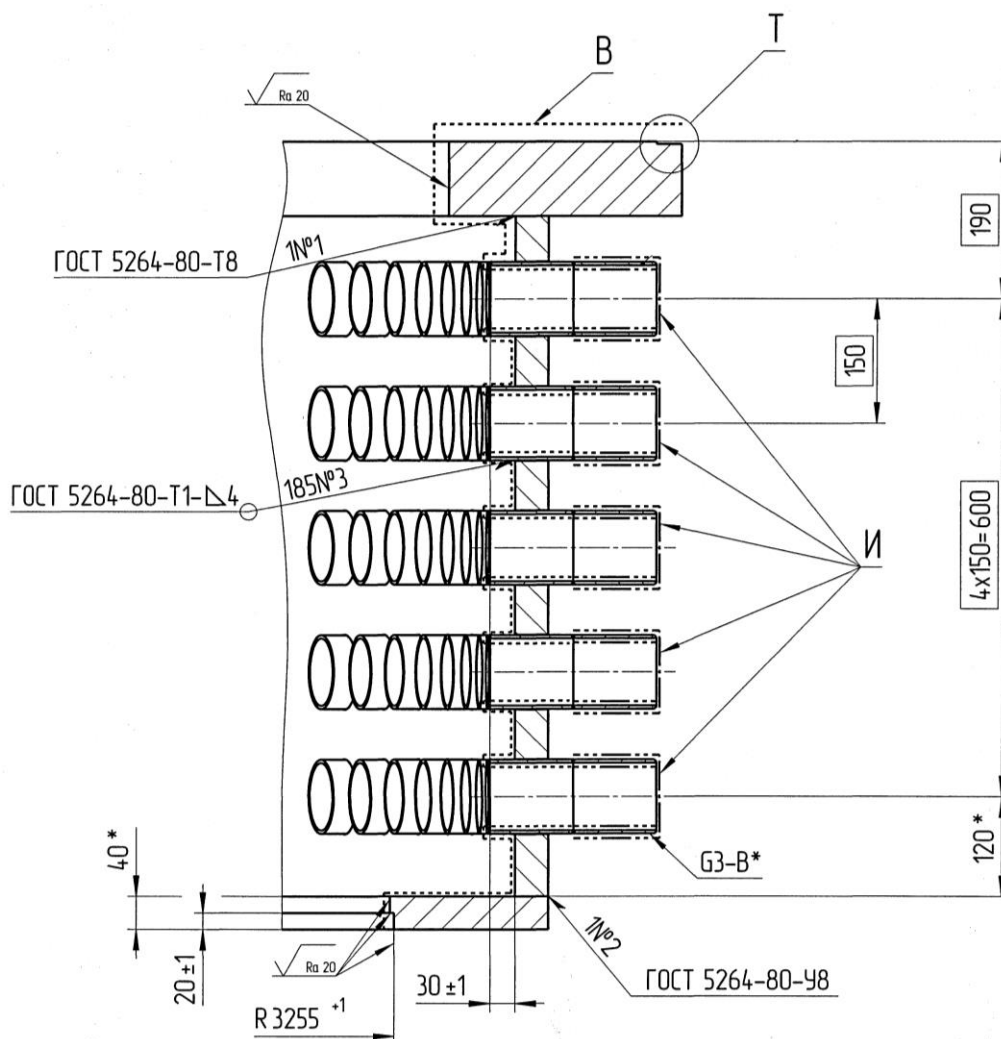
Сварные швы при сборке и сварке опоры проставки в сборе
